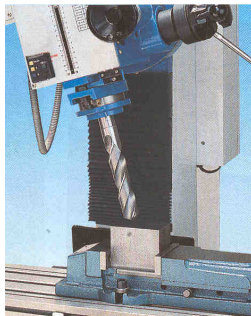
a Strojový zverák s vymeniteľnou prizmatickou čeľusťou
